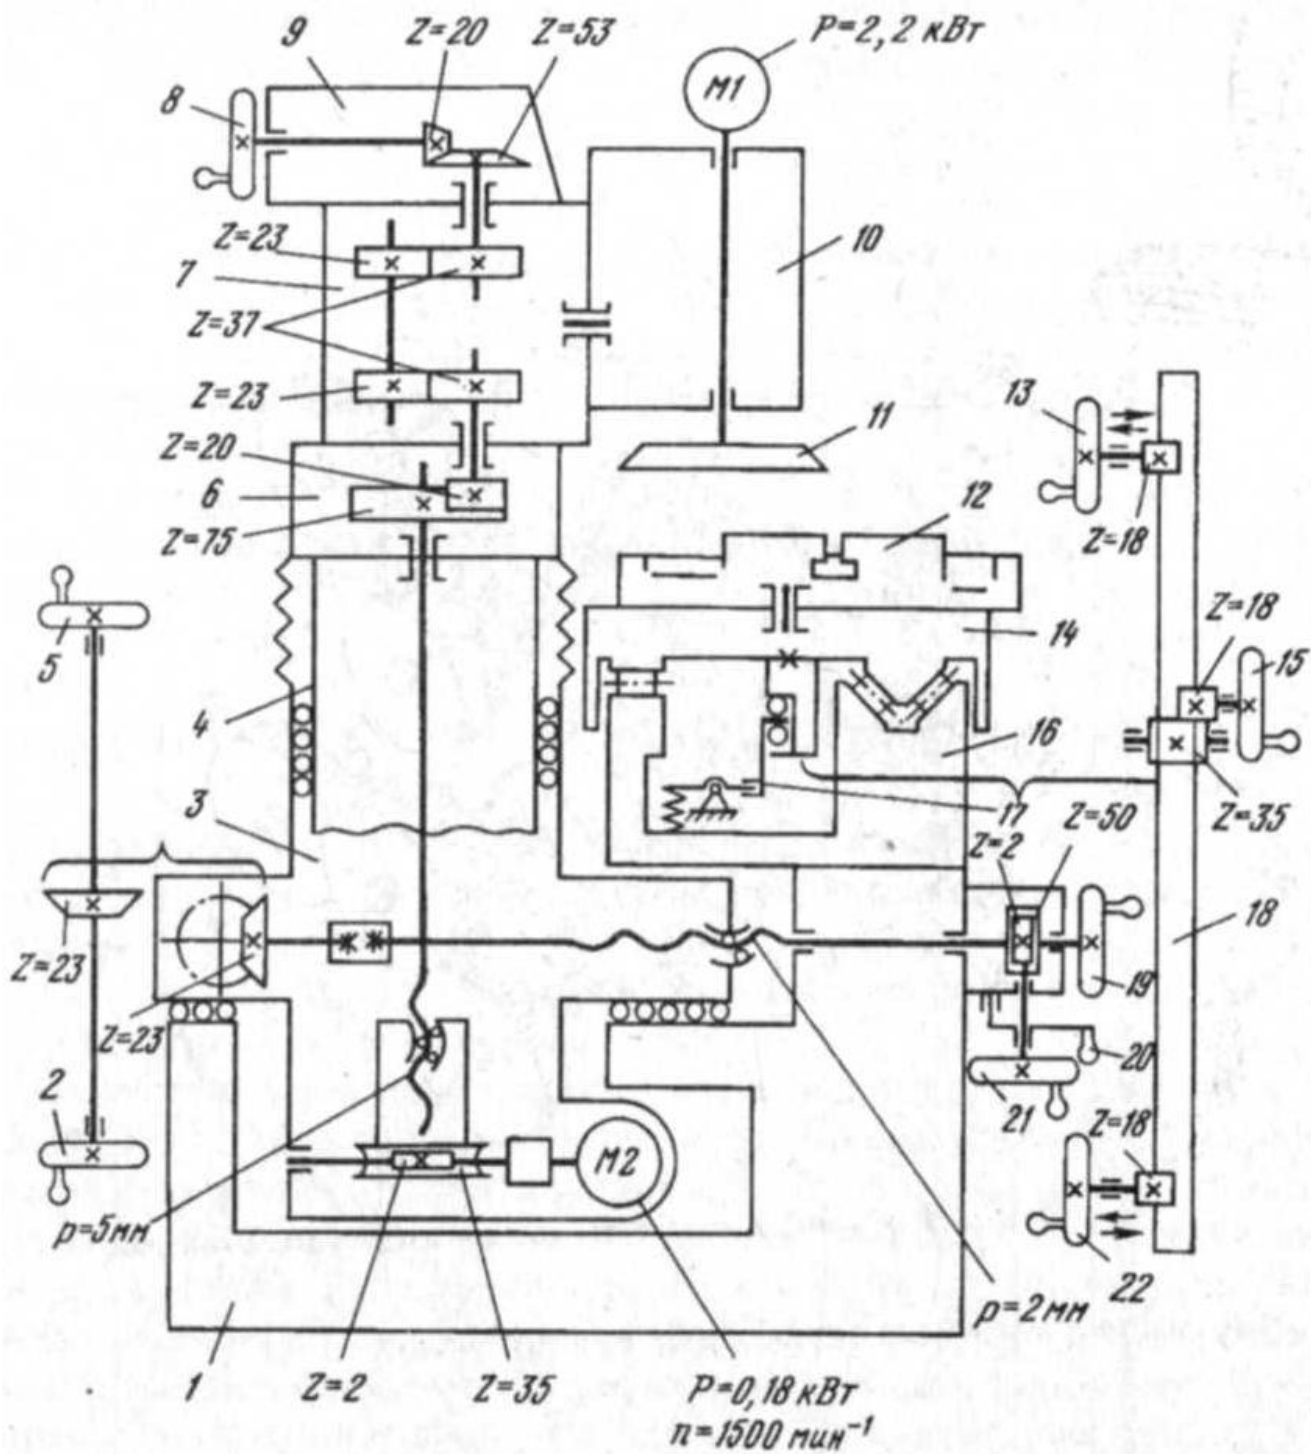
Компоновочно - кинематическая схема универсально-заточного станка модели 3Е642.
